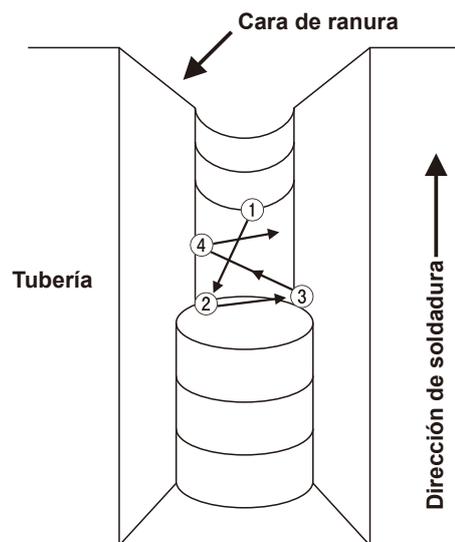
La Técnica del Paso Anterior en Posición Vertical-Arriba Soldadura de tuberías
